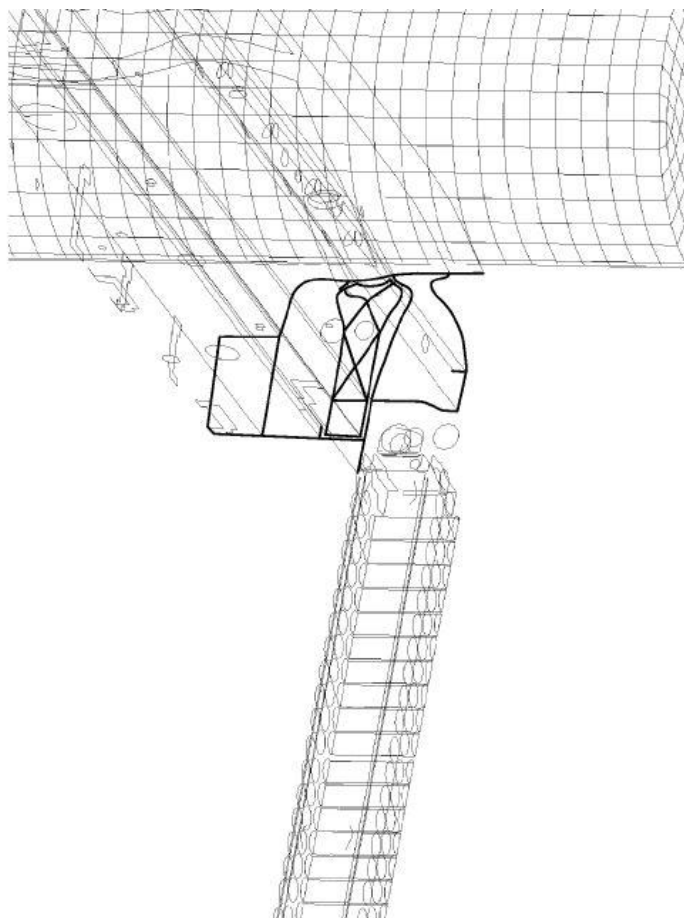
Sistem za povezivanje modulu i prigušenje vibracija [11]
